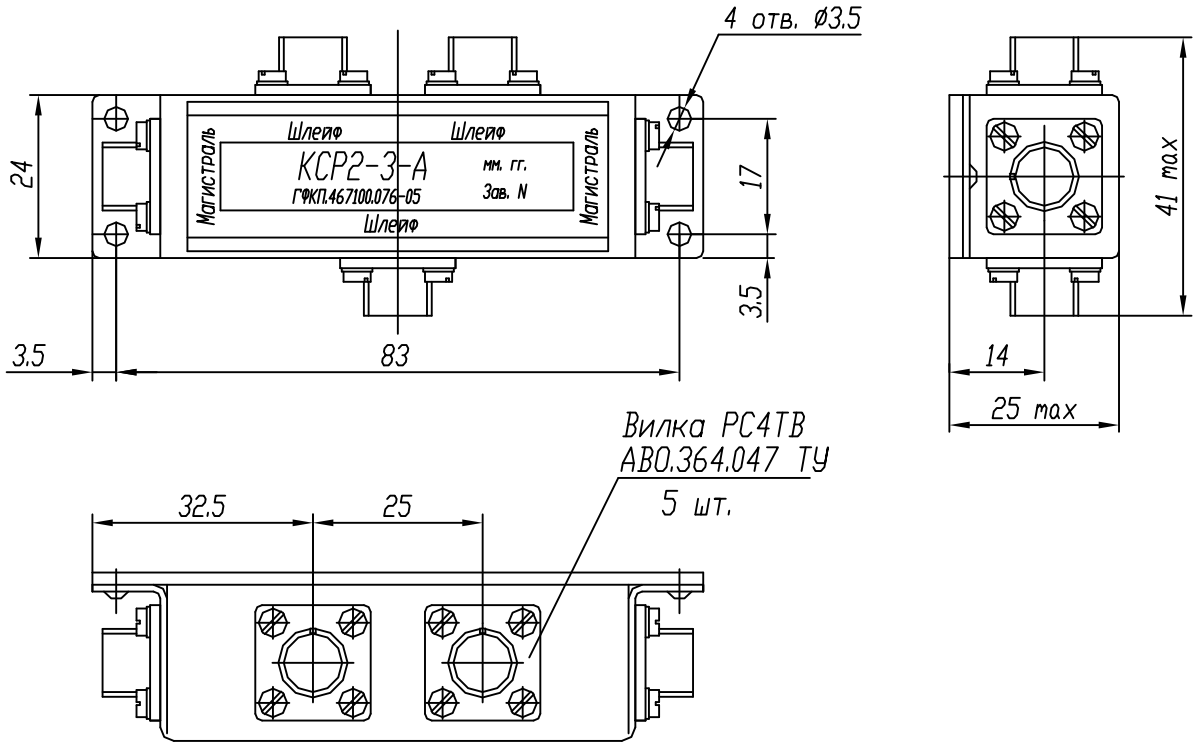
Габаритный чертеж коробки КСП2-3-А
